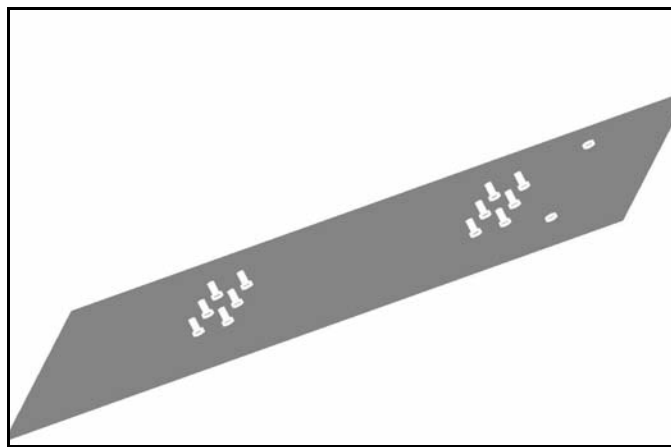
Planta do pé, com os furos necessários para fixação de componentes.
